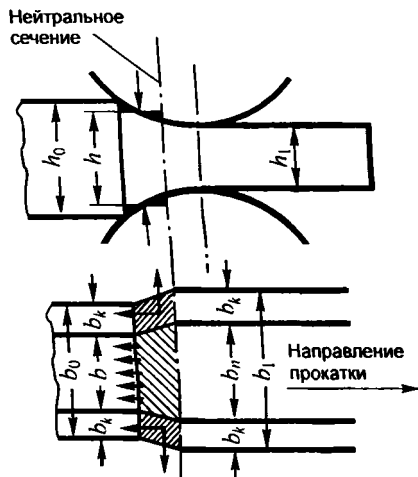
Влияние прилипания заготовки к валкам на уширение
